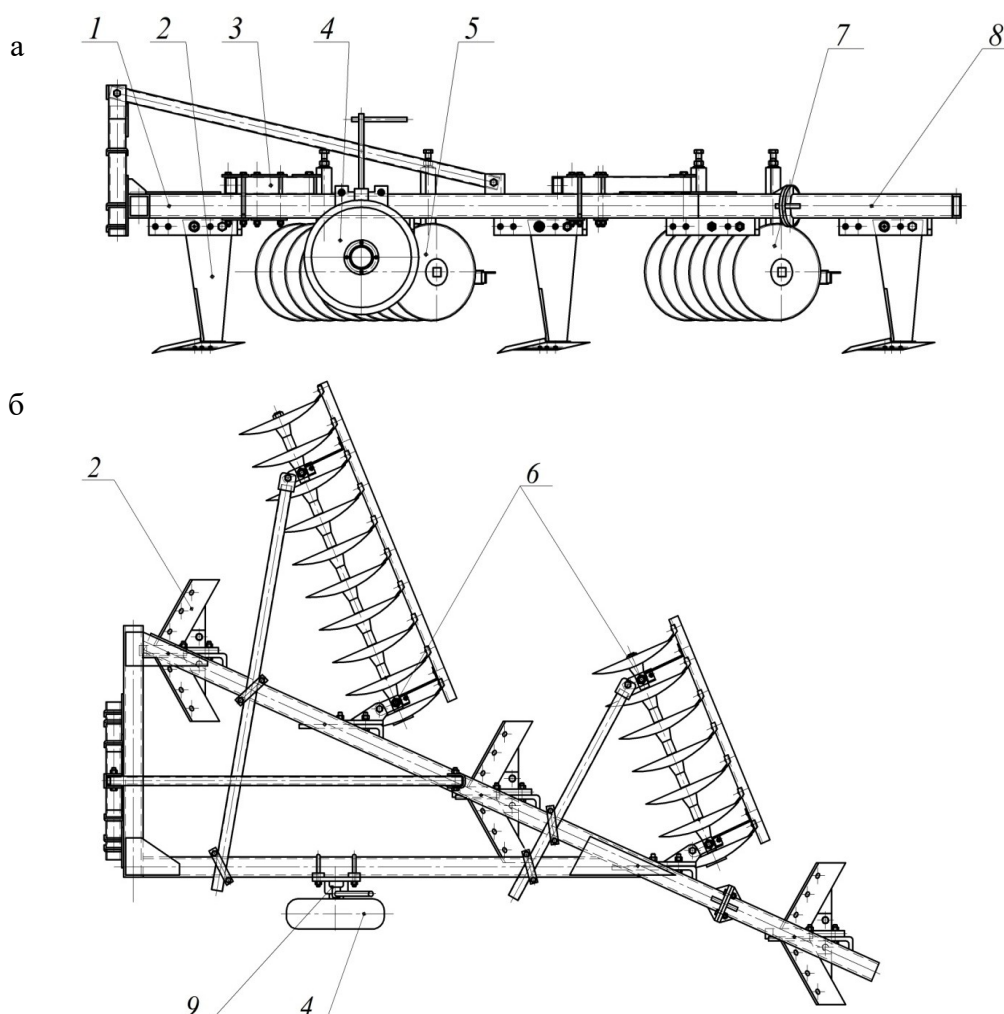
Плуг-плоскорез ППН-4-35/3-70 со сменными рабочими органами для безотвальной обработки почвы: 1 - рама; 2 - лапа плоскорезная; 3 - выносная балка; 4 - опорное колесо; 5 - основная дисковая секция; 6, 9 - механизмы регулирования глубины обработки; 7 - дополнительная дисковая секция; 8 - удлинитель
